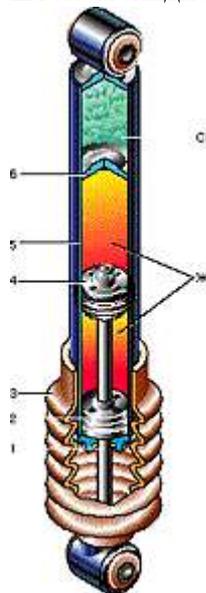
Схема газонаполненного амортизатора: 1 — шток; 2 — уплотняющий и направляющий узел штока; 3 — чехол или кожух; 4 — поршень с системой клапанов; 5 — рабочий цилиндр; 6 — разделительный поршень; Ж — жидкость; СГ — сжатый газ.
